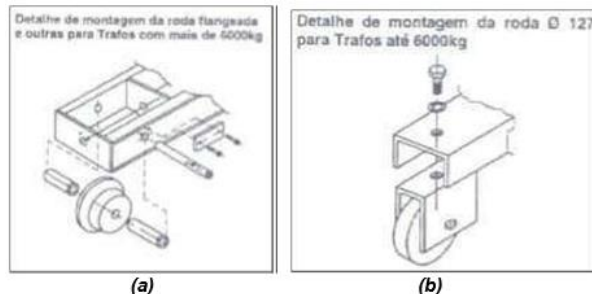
Exemplo de rodas; a) Flangeada; b) Lisa
